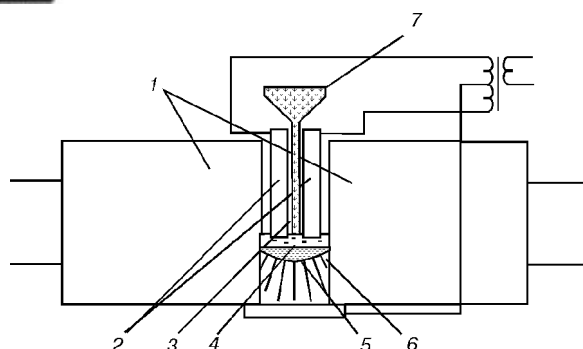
Схема электрошлаковой бифилярной сварки двумя неподвижными электродами с подачей в сварочный зазор с помощью дозатора кусковых присадочных материалов: 1 — свариваемые заготовки; 2 — неподвижные расходные электроды; 3 — кусковой присадочный материал; 4 — шлаковая ванна; 5 — металлическая ванна; 6 — сварочный шов; 7 — бункер для подачи кускового присадочного материала
